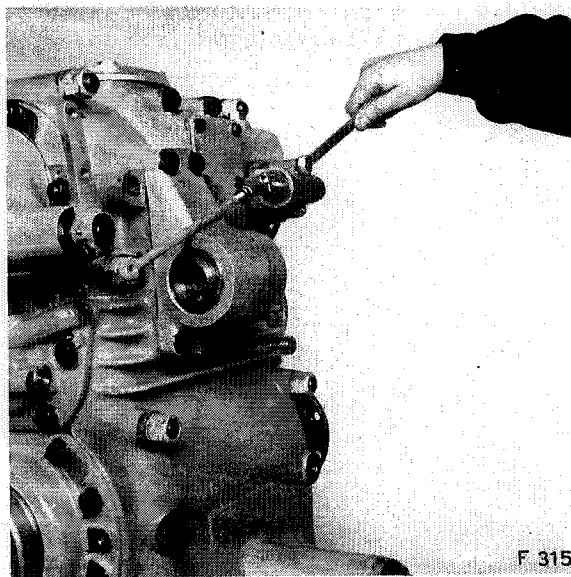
Lösen der Schrauben des Supports für die Verriegelung Seilwinde / Räderantrieb
